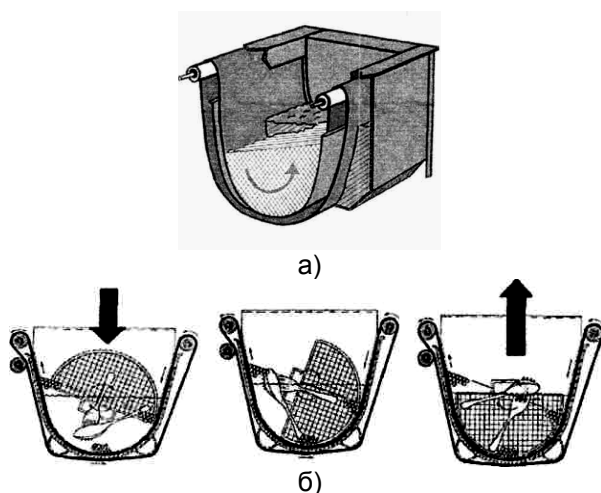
Внешний вид контейнера (а) и этапы извлечения деталей (б)
